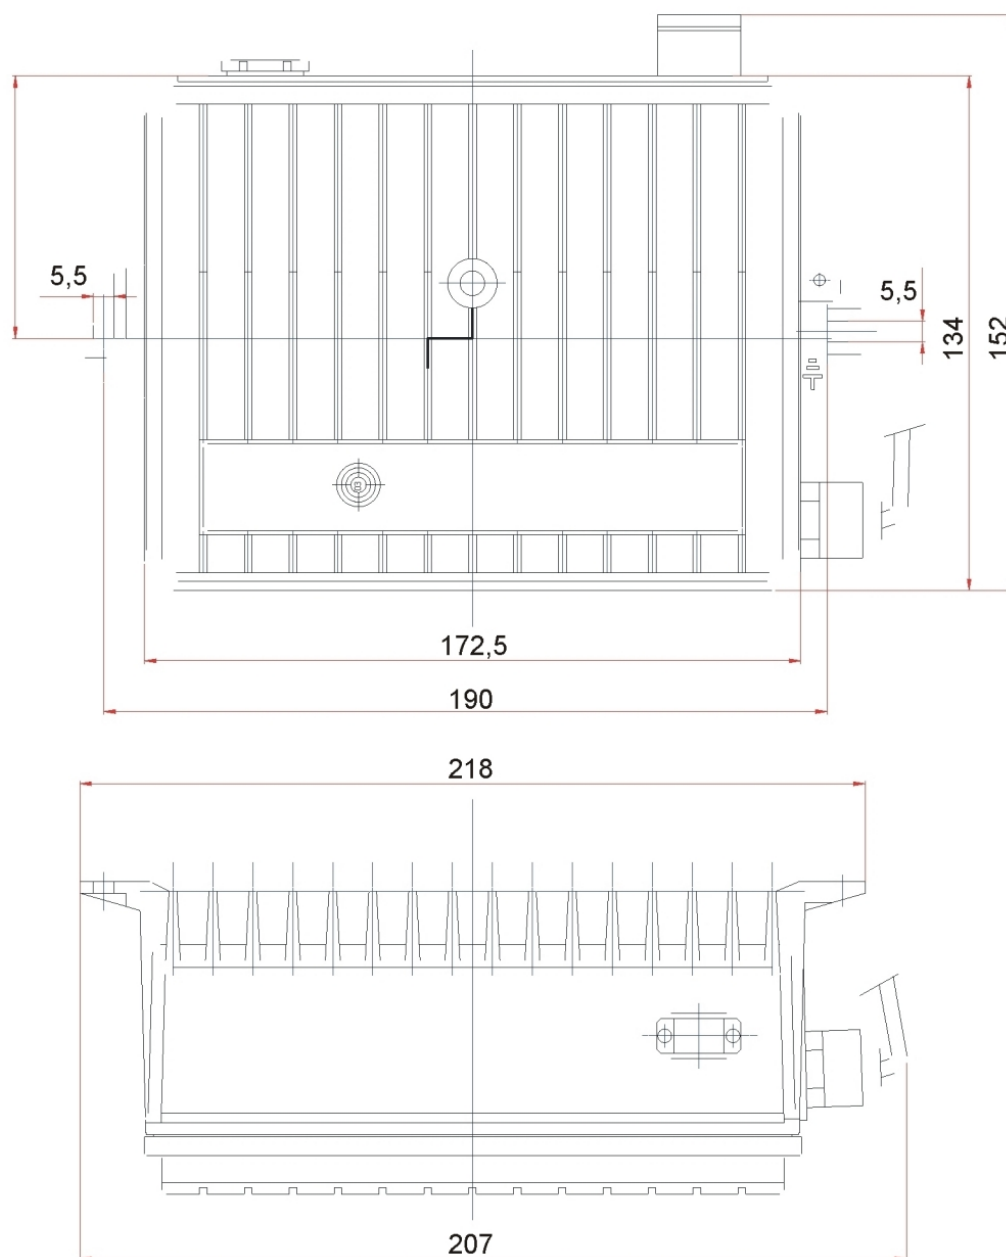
Вид корпуса оптического приемника LAMBDA PRO 50.
